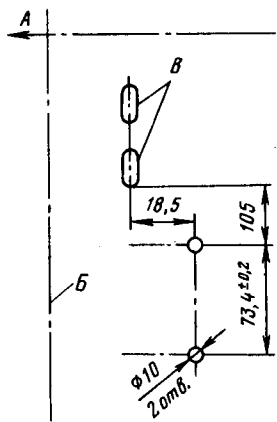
Схема расположения отверстий в полу кузова для крепления регулятора давления (вид сверху):
